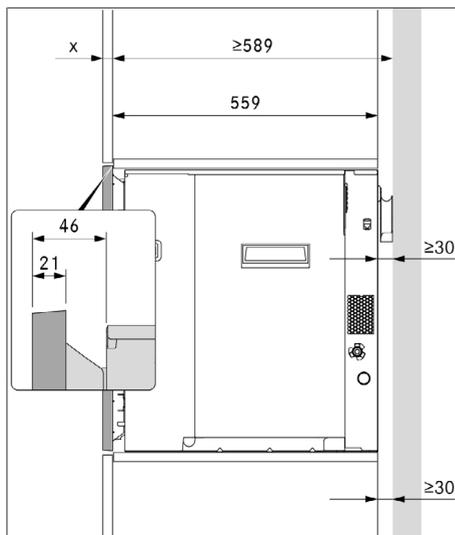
Dimensões de instalação sem estrutura de espaçamento
